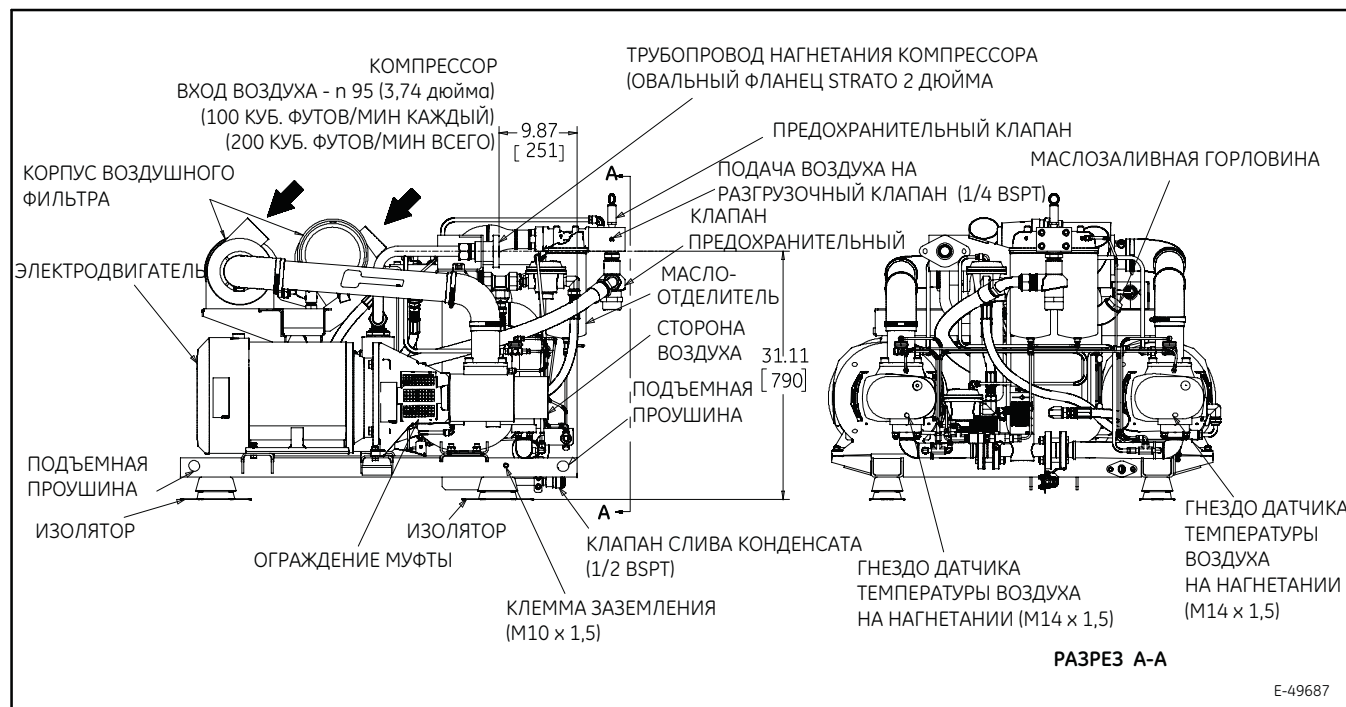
Конструкция воздушного компрессора локомотива ES44ACi.
